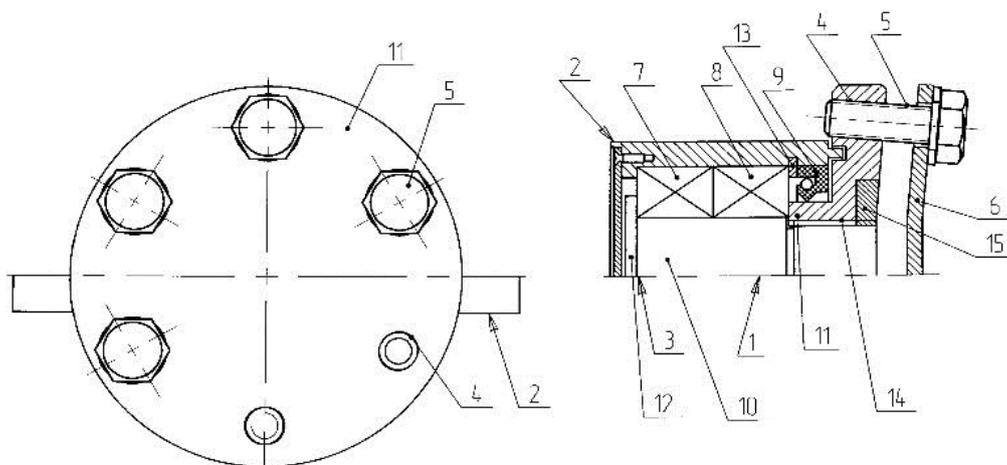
Подшипниковый узел дискового почвообрабатывающего орудия
